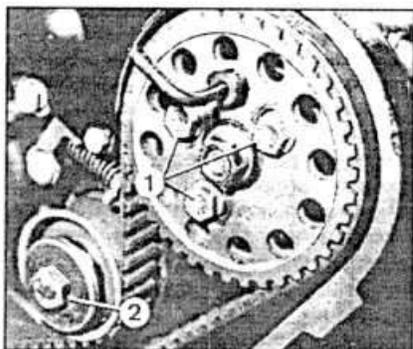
Е.14. Установка приспособления для регулировки топливного насоса.
